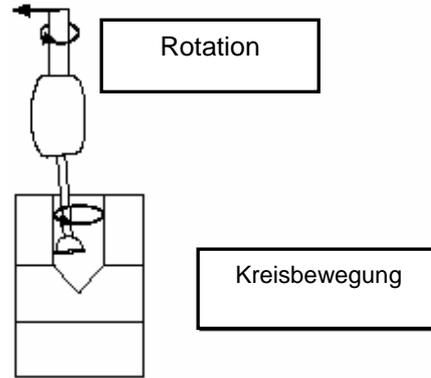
Das Werkzeug ins Zentrum der zweiten Bohrung bewegen. Rotation und Kreisbewegung des Werkzeugs stoppen.
